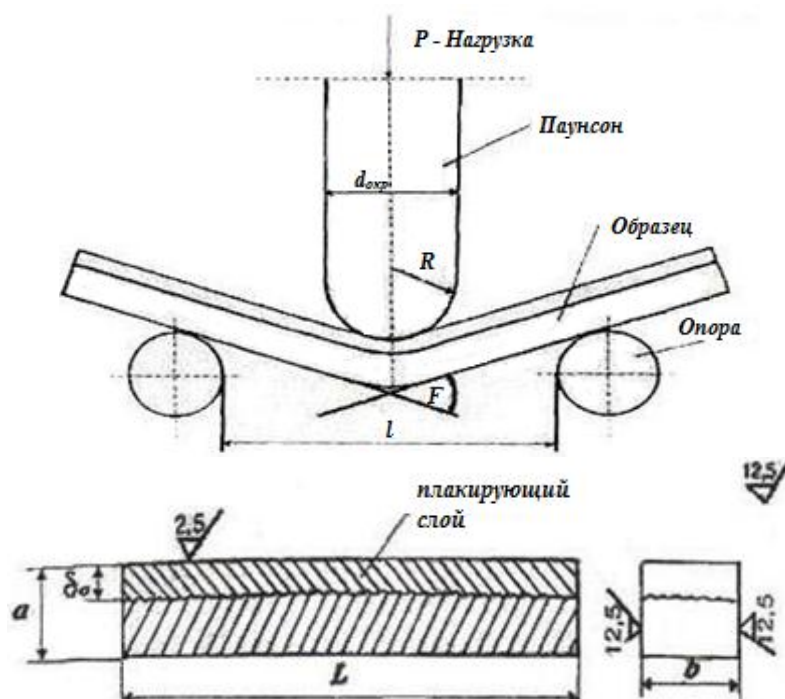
Образец и схема испытаний плакированной стали на изгиб
